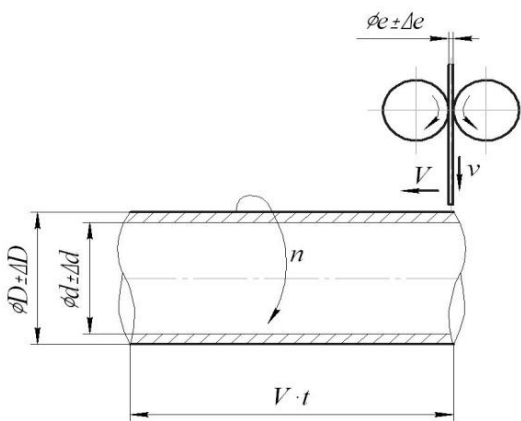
Схема наплавлення циліндричної заготовки дротом суцільного перетину
